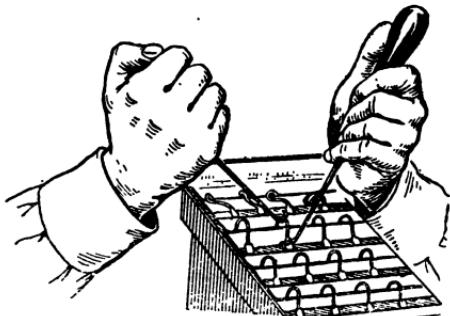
Инструмент для укладки и правки монтажа.
